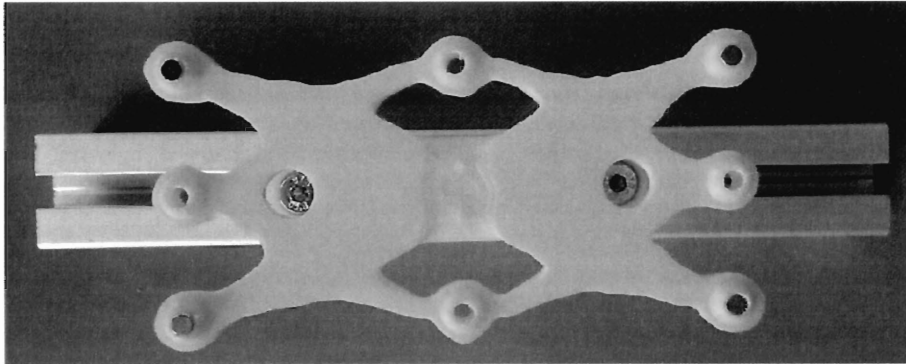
Element de prindere montat pe profil de aluminiu – TIP 2
